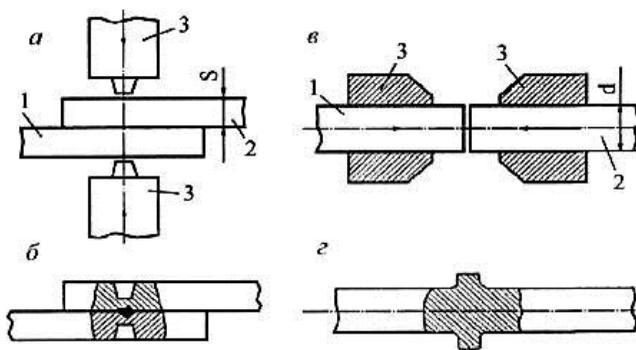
Схемы холодной сварки: а, б – точечной; в, г – стыковой; 1, 2 – свариваемые детали; 3 – пуансоны; а, в – положение перед сваркой; б, г – после сварки
